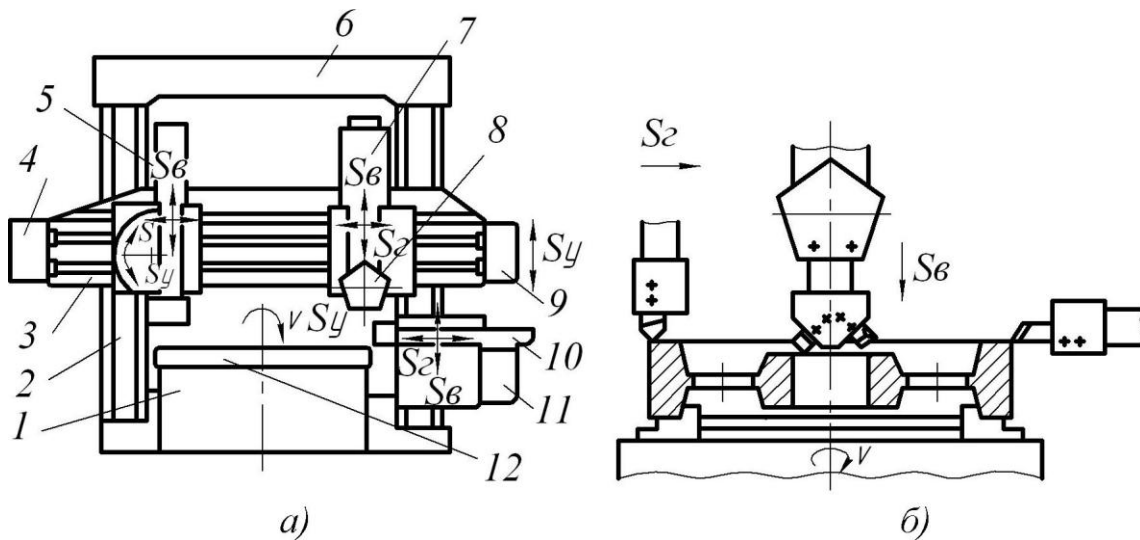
Схеми токарно-карусельного верстата (а) і обробки на ньому заготовки (б)
